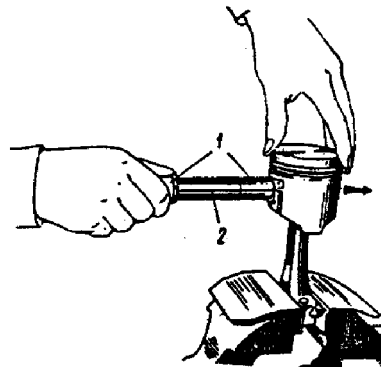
Instalação do pino do êmbolo: 1 - dispositivo 02.7853.9500; 2 - pino do êmbolo.
